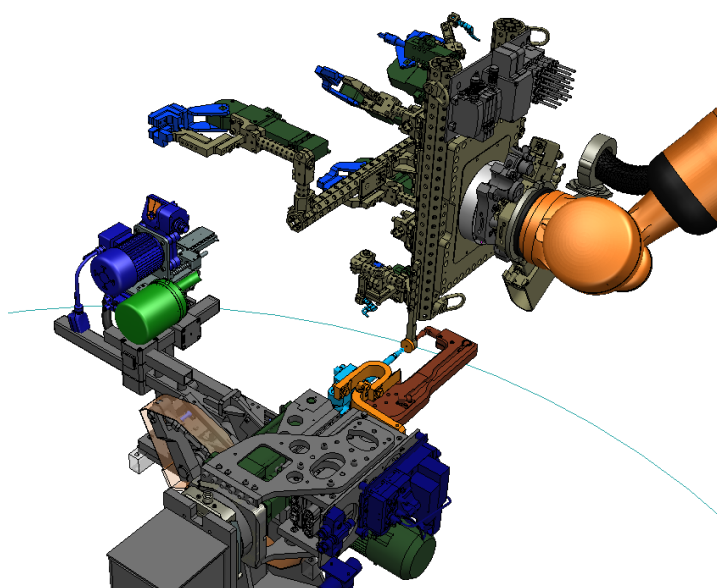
Положение для калибровки сварочного пистолета робота 5080R03 Z
